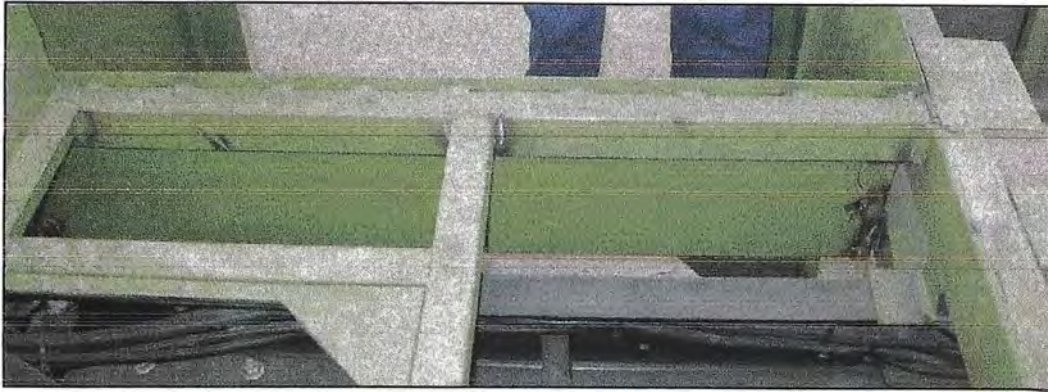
Estructura amarrada vía soldadura MIG.
